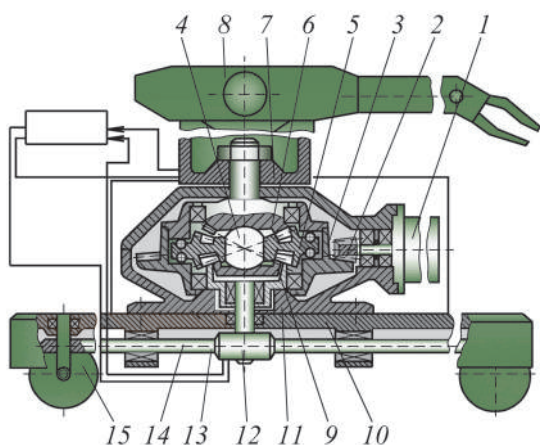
Robot mobil cu transmisie precesională [25]
